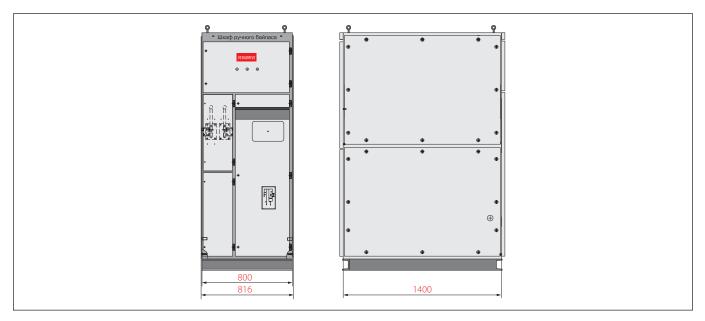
Корпус шкафа ручного байпаса типоразмера МВ01
